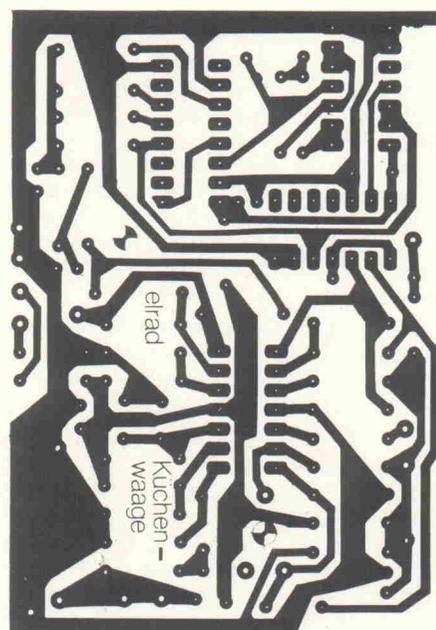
Das Platinen-LAYOUT für die Küchenwaage
